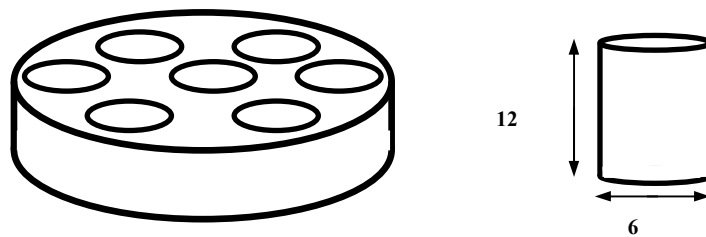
Molde y probeta de ensayo mecánico de compresión.
